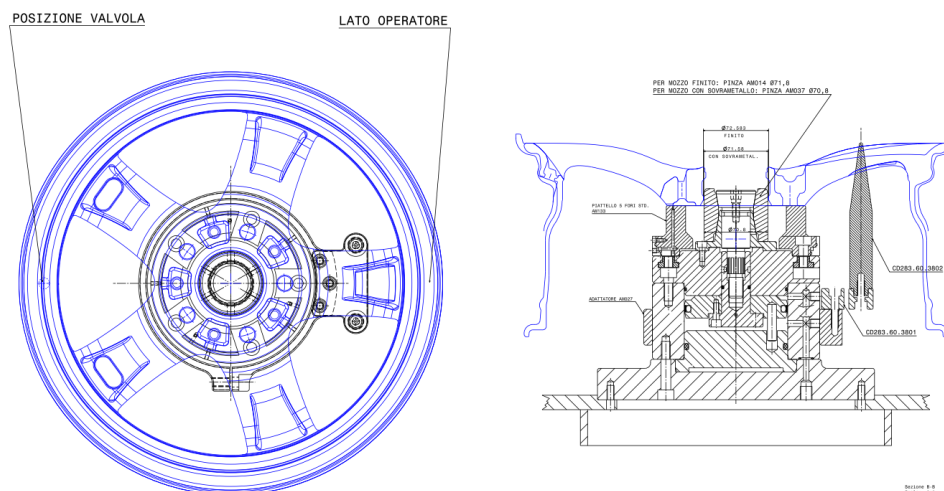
Upnuté ohrubované kolo [zdroj: autor]
